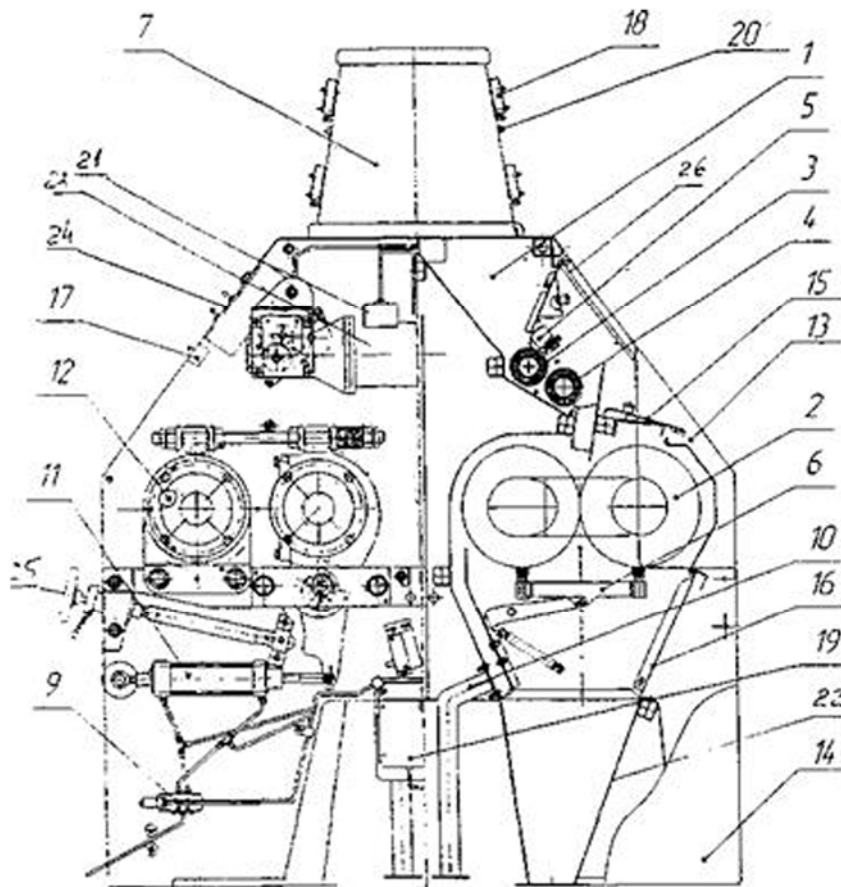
Вальцьовий верстат типу ВС:
